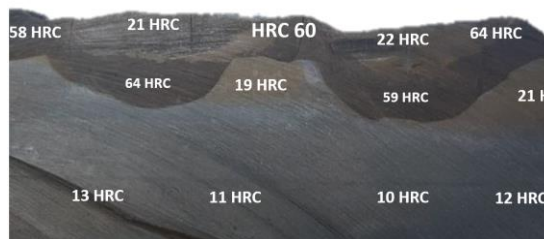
Твердость наплавленного и основного металла при однослойном и двухслойном нанесении покрытия
